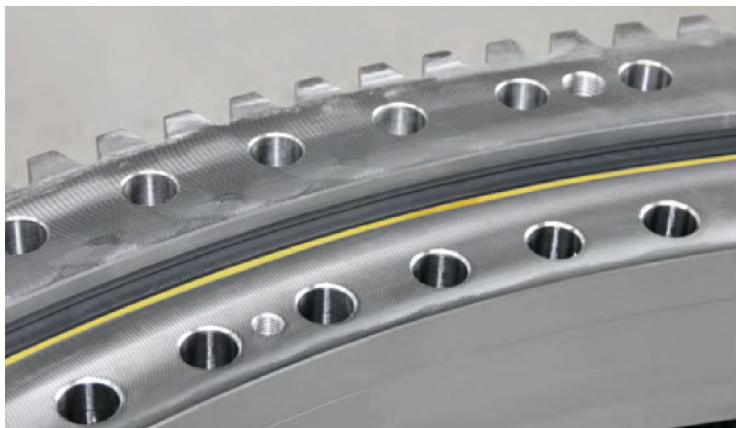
Geschlossener Fettkragen an Lagerdichtung
